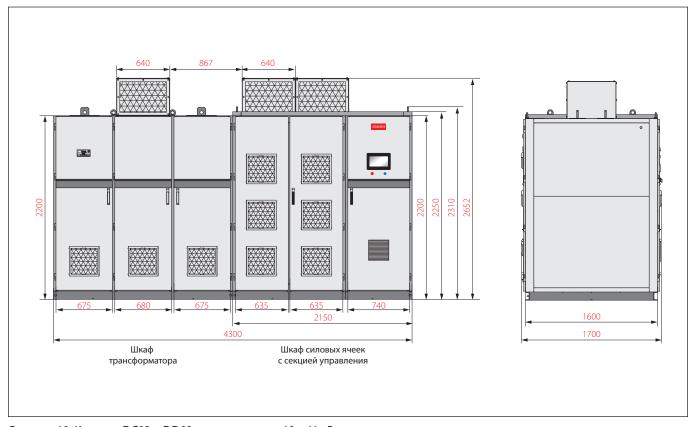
Корпуса DC01 и DD01 на напряжение 10 и 11 кВ
